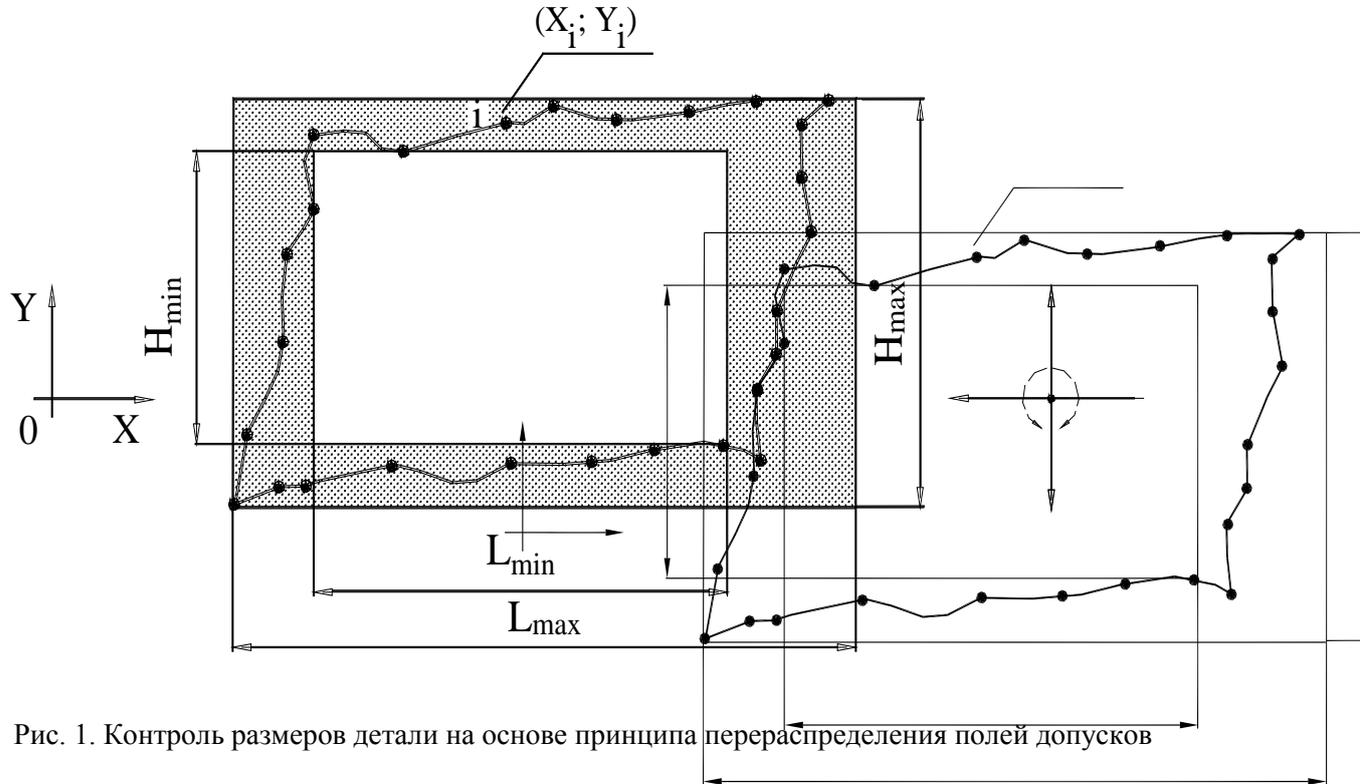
Контроль размеров детали на основе принципа перераспределения полей допусков
